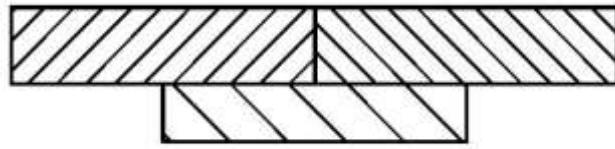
Нанесение штриховки на деталях сборочного чертежа
